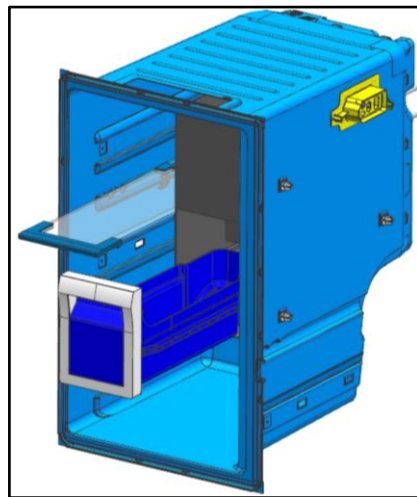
Buz makinası şasisinin çoklu kullanım bölmesine montajı.
